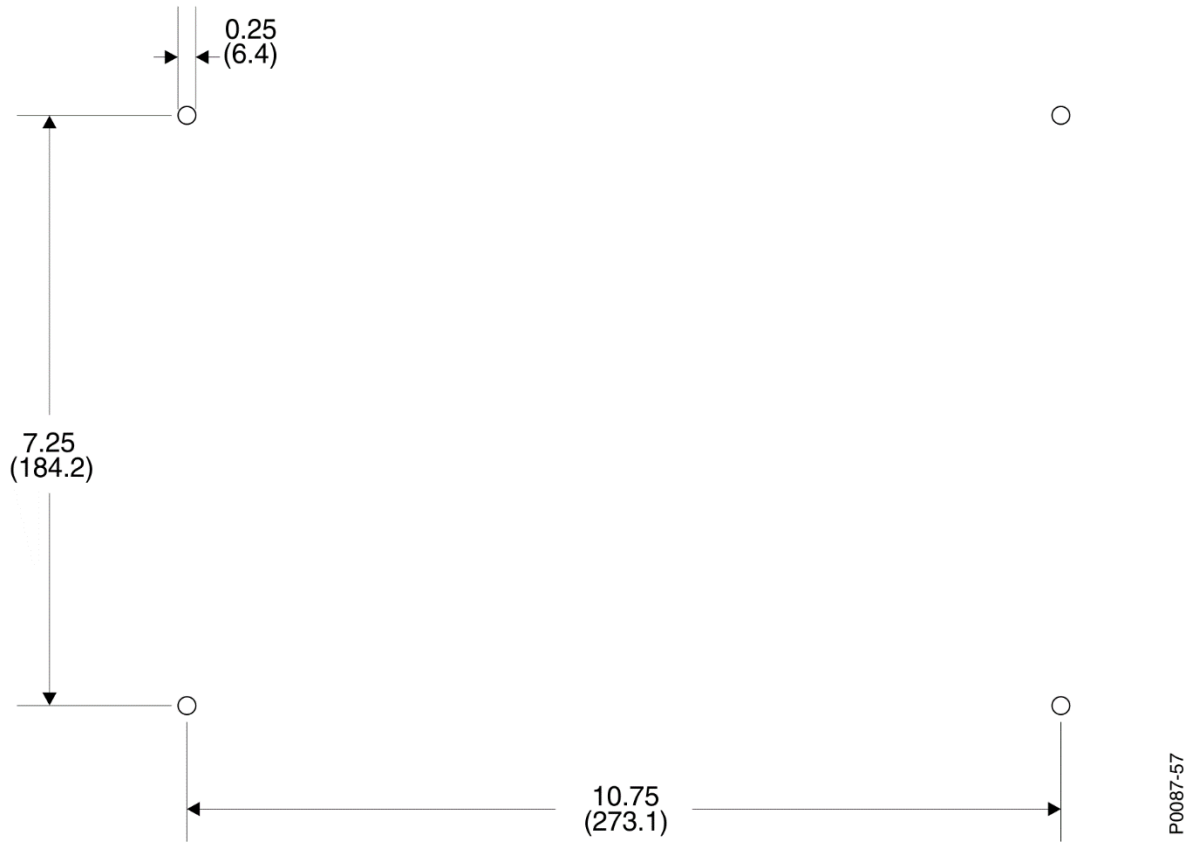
后面板钻孔尺寸, 型号 xPxxxxxxx
